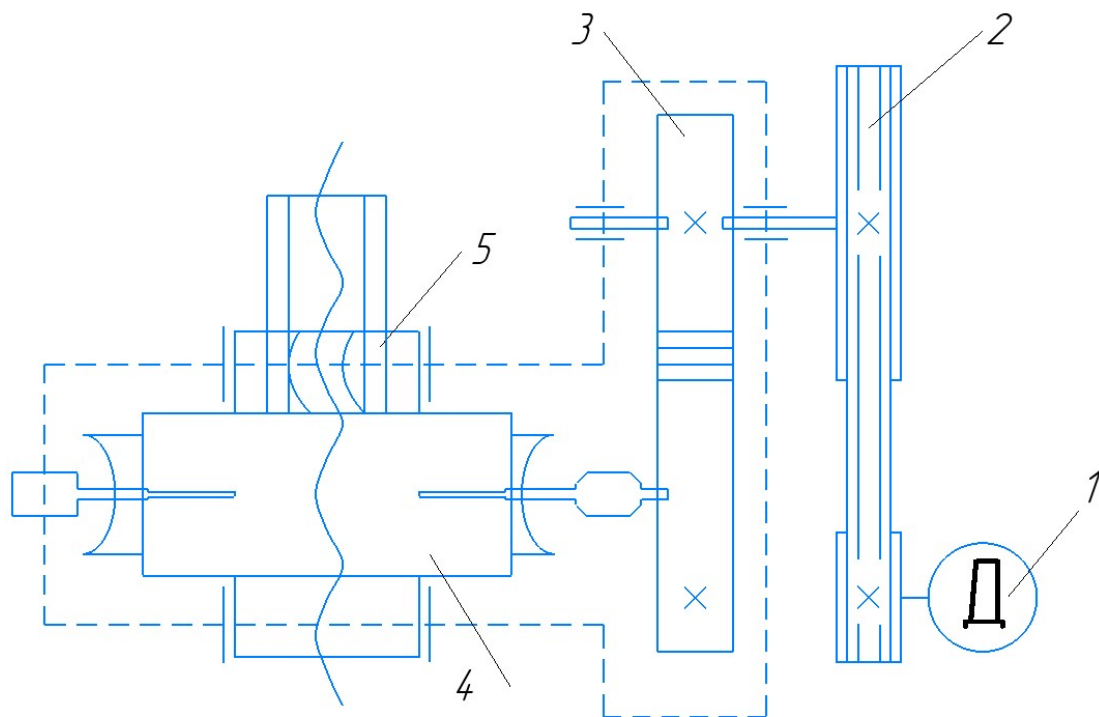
Кінематична схема приводу: 1 - двигун, 2 - клинопасова передача, 3 – циліндрична косозуба передача; 4 – черв'ячна передача, 5 - гвинт.
